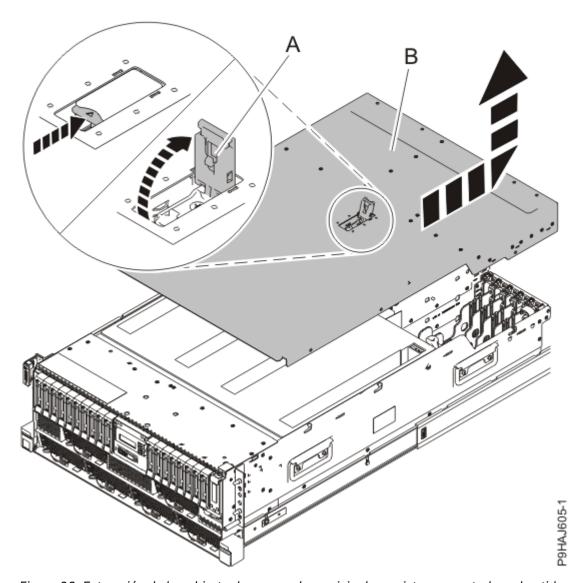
Extracción de la cubierta de acceso de servicio de un sistema montado en bastidor
